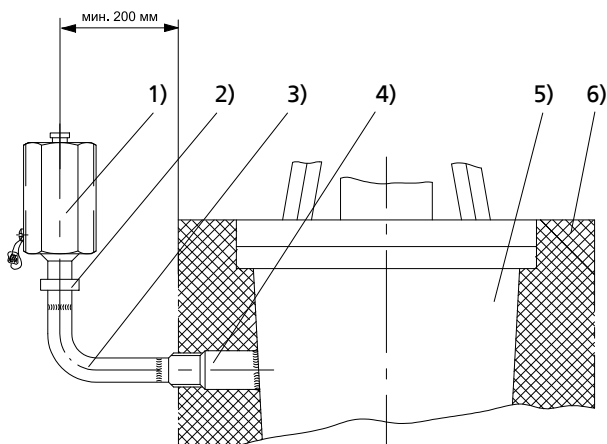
Устройство защиты корпуса от избыточного давления UGS/UGSV на запорной задвижке с самоуплотняющейся крышкой
